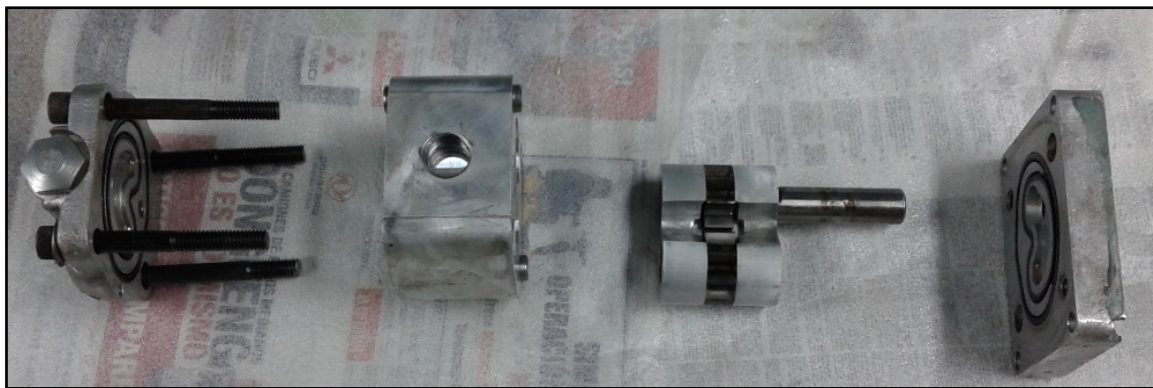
Despiece de bomba de engranajes externos de caudal fijo.
